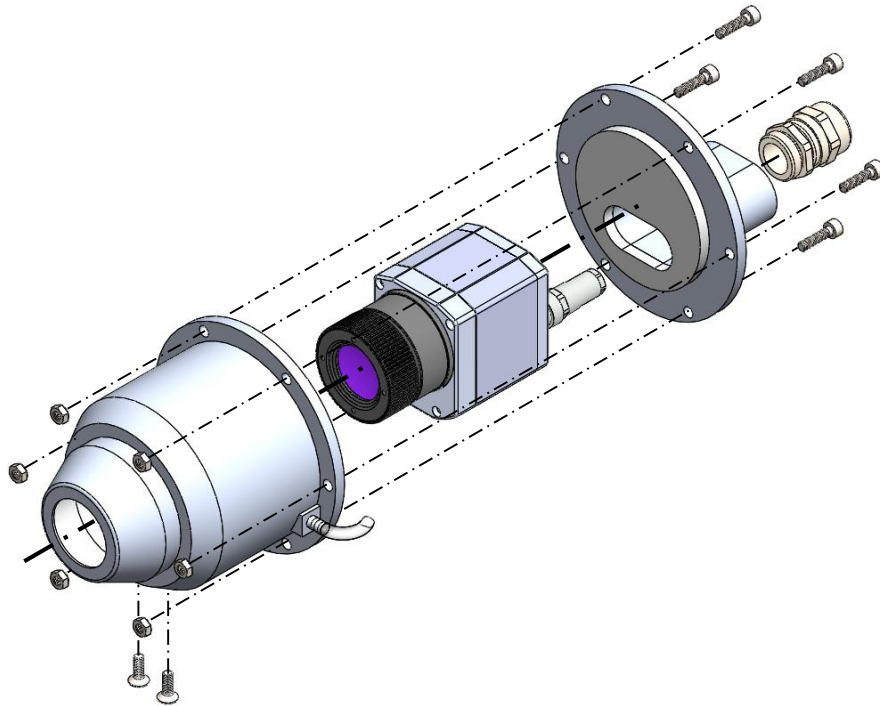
Vista explodida do conjunto PI 450 G7 e caixa de refrigeração
